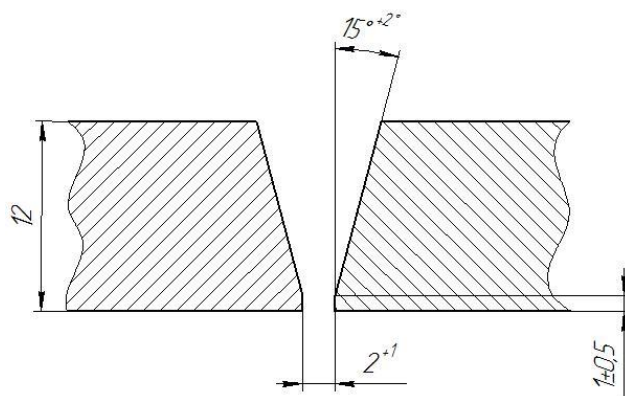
Подготовка под сварку труб диаметром 325 мм толщиной стенки 12 мм
